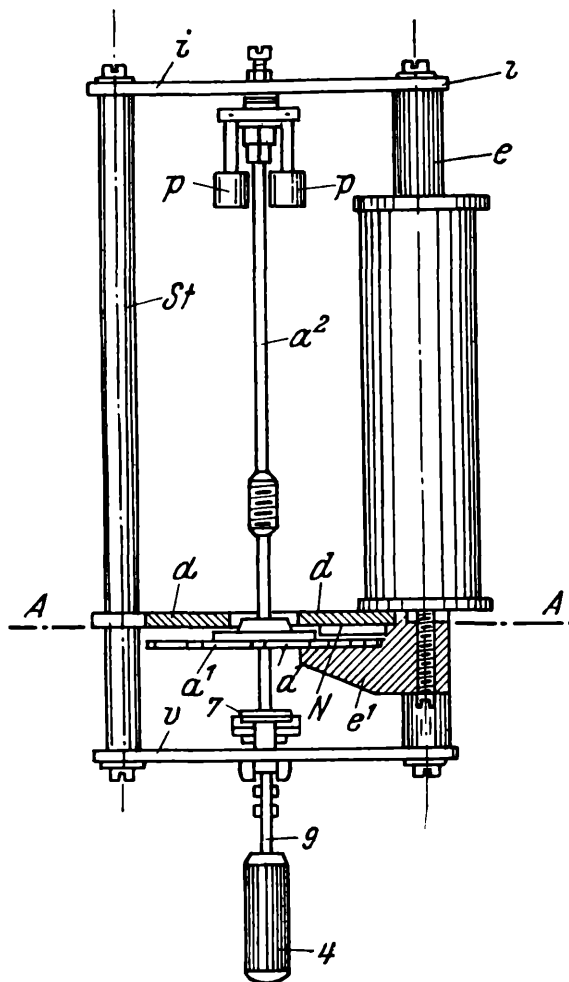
Michl-Uhr mit Anwerfmotor, Seitenansicht
